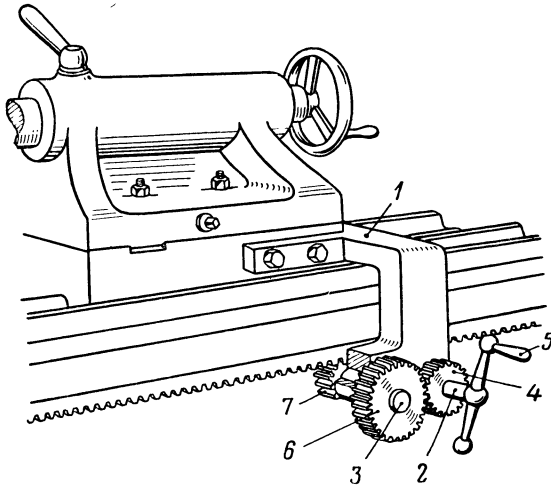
Приспособления для закрепления сверла при механической подаче.
